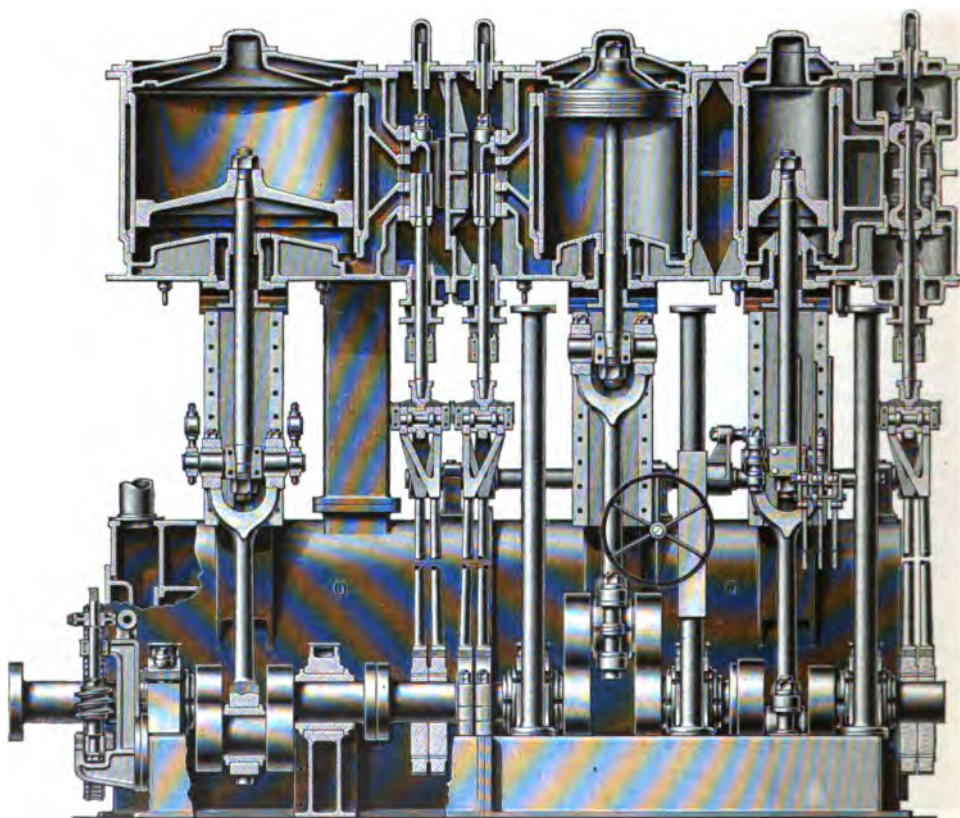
Dreifach-Expansionsmaschine, Längenschnitt.
